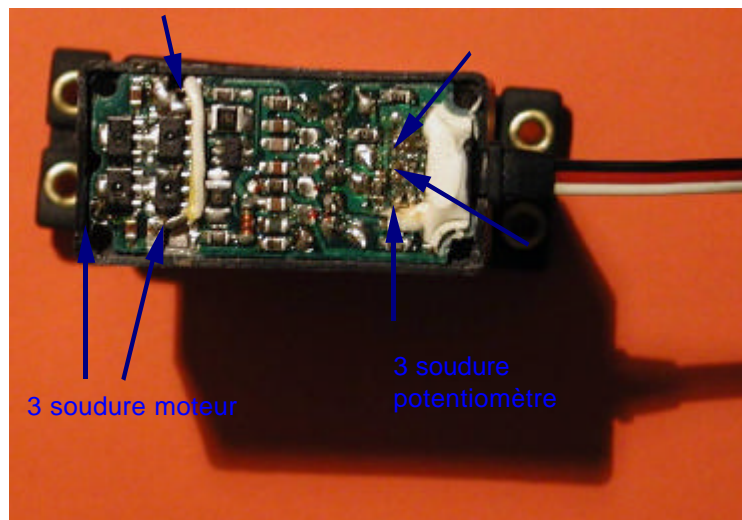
, remettre la platine. Position des 6 soldures à refaire et du fil électrique additionnel.
